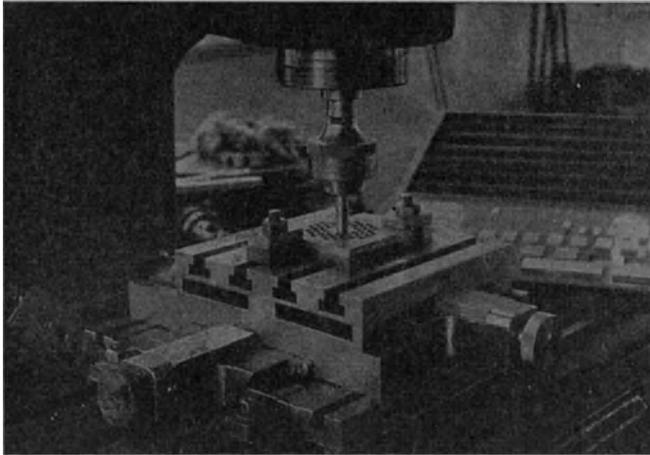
Einstellung einer Schnittplatte mittels Endmaßen auf der Bohr- und Fräsmaschine.
